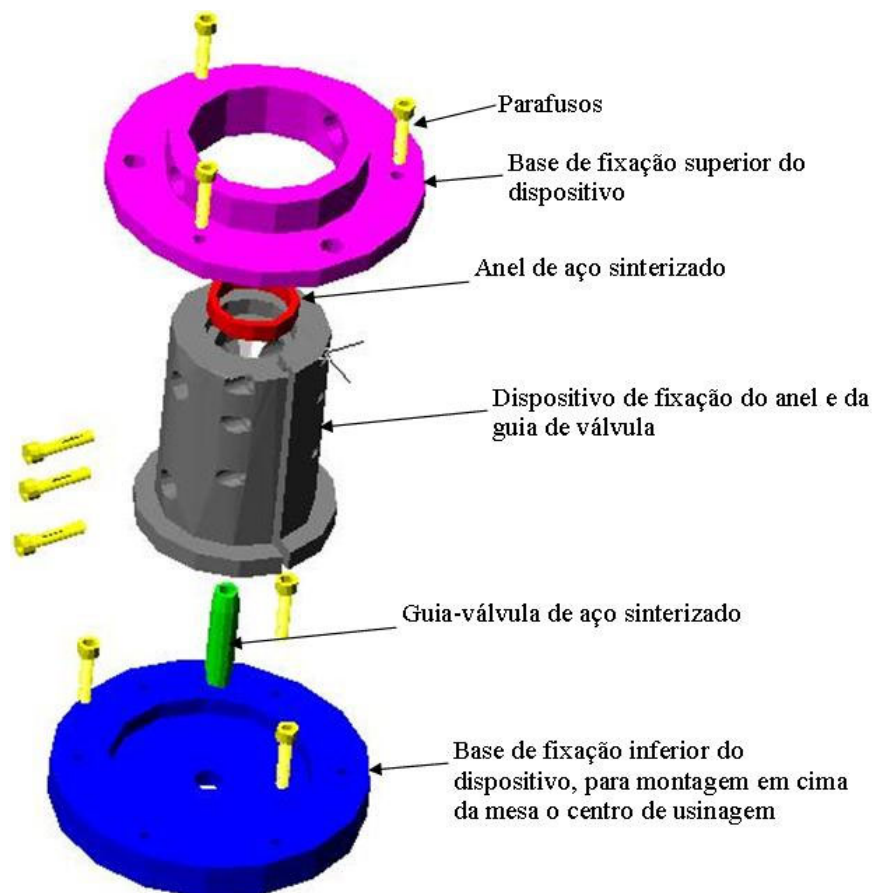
Desenho esquemático do projeto do dispositivo de fixação do anel e guia de válvula
